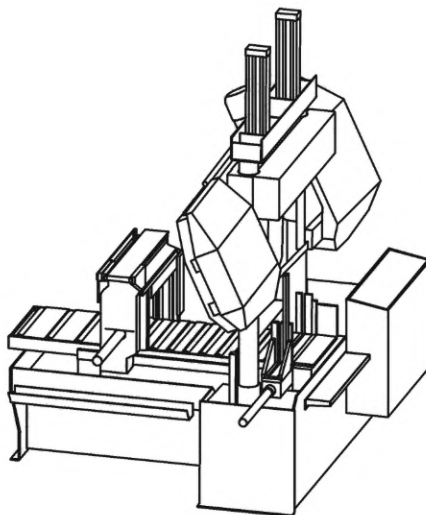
Автоматический горизонтальный ленточнопильный станок — колонный тип
